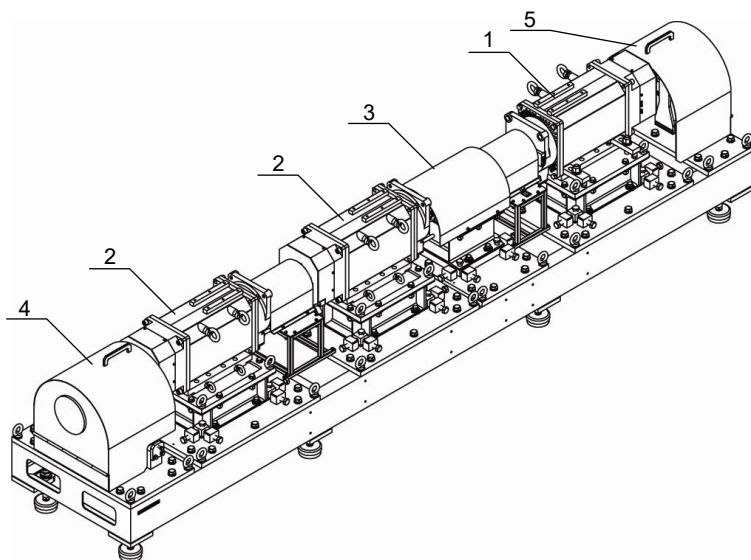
Общий вид рабочей зоны стенда для проверки двигателя
